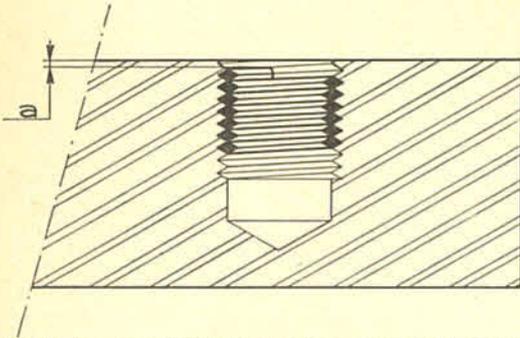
Einsatzposition des Gewindes $a = 0,5 \times \text{Steigung des Gewindes}$
